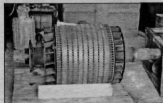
Ротор електродвигуна з відновленими посадочними поверхнями під підшипники. Відновлення здійснено шляхом газопорошкового наплавлення порошком ПГ-12Н-01.
